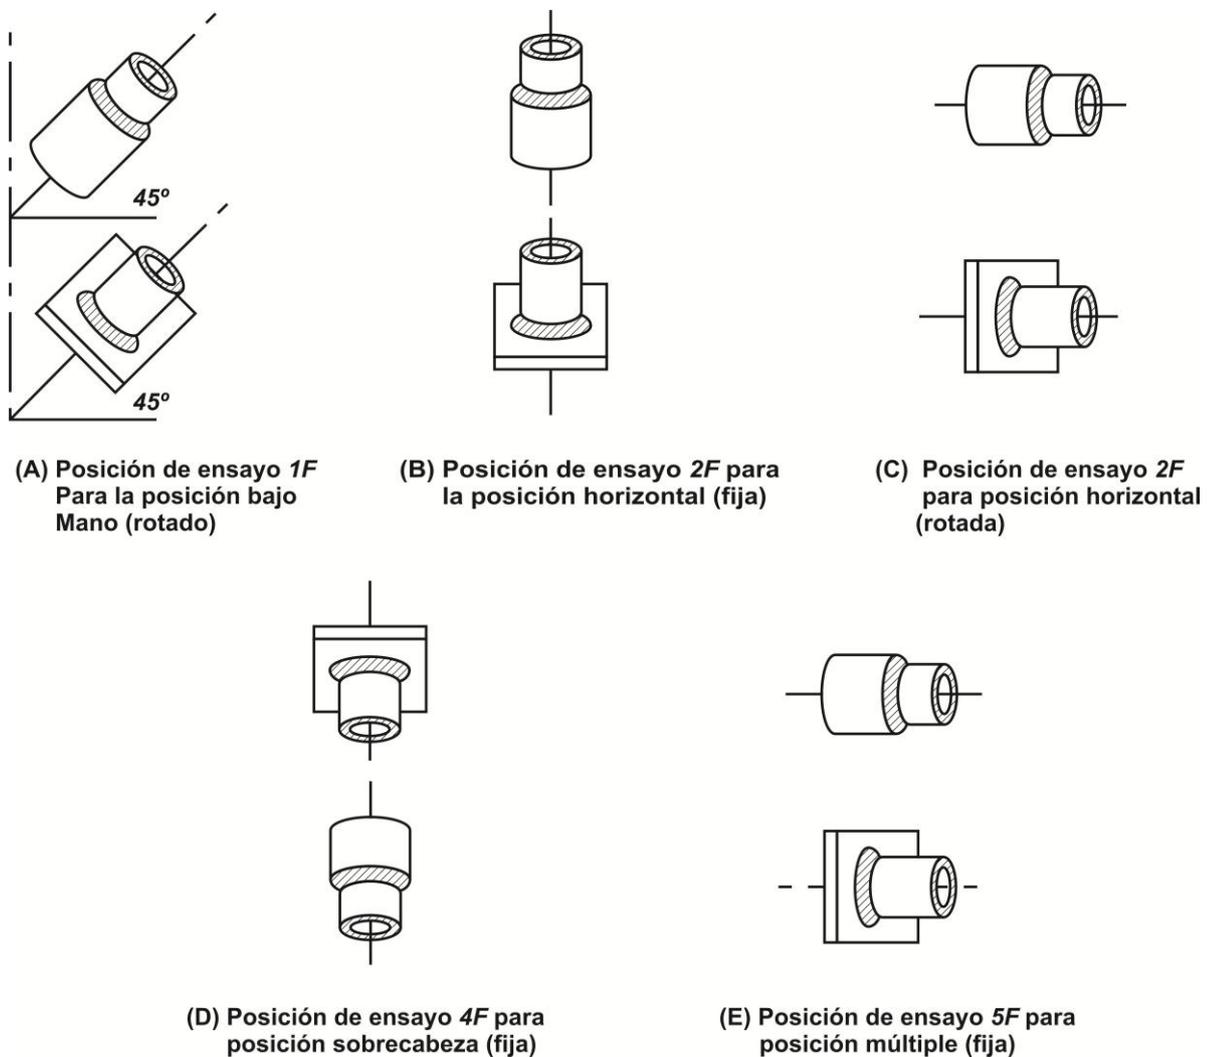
Posiciones para ensayo de tubos o caños para soldadura de filete.
